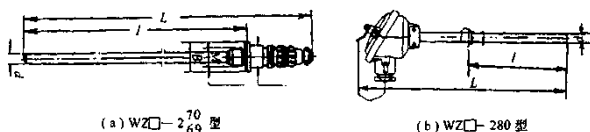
WZ□-269,270,280 型热电阻外形尺寸图
